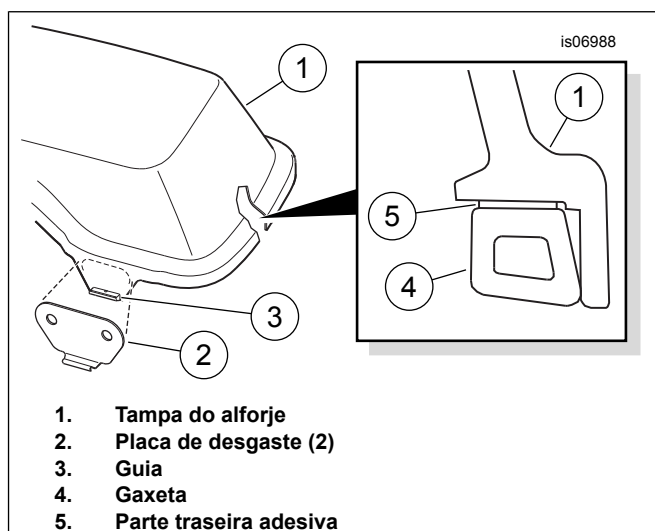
Montagem das placas de desgaste e da gaxeta na tampa do alforje
